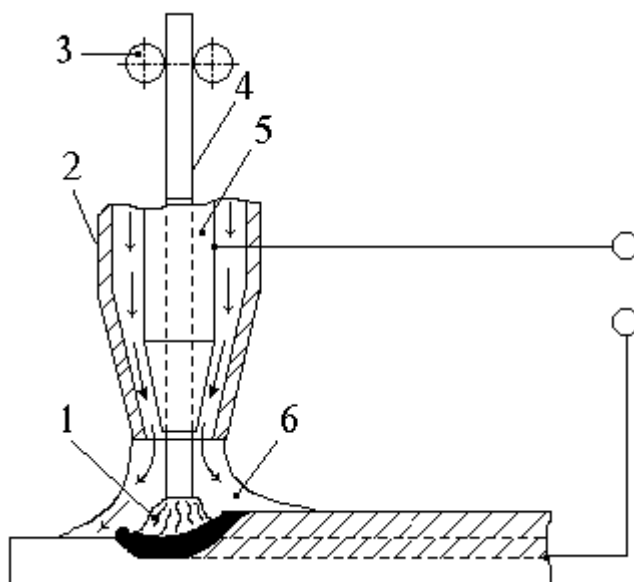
Дуговая сварка в защитном газе плавящимся электродом: 1 – электрическая дуга; 2 – газовое сопло; 3 – подающие ролики; 4 – электродная проволока; 5 – токоподводящий мундштук; 6 – защитный газ
